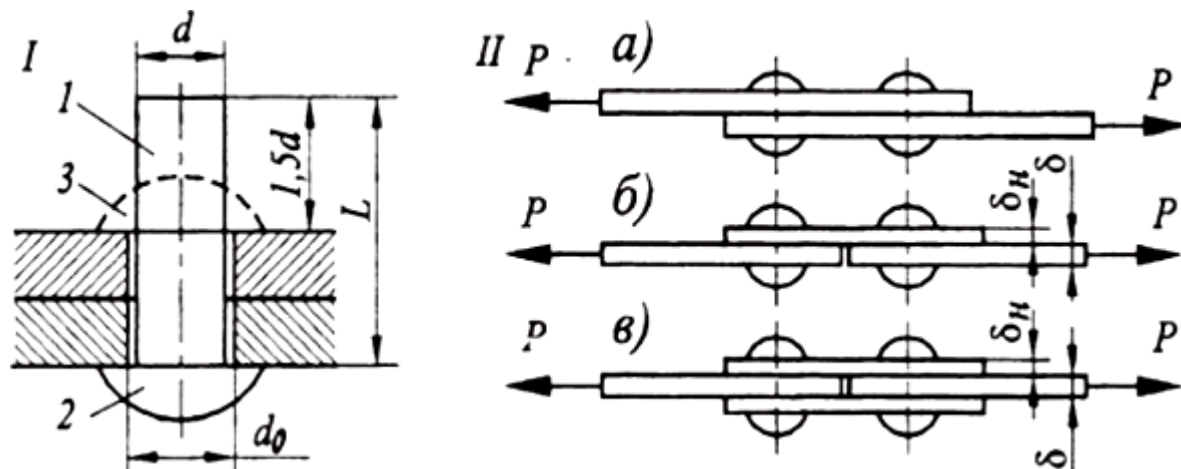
Конструкция заклепочного соединения (I) и схема приложения нагрузки (II) к основным и накладным пластинам пластинами
